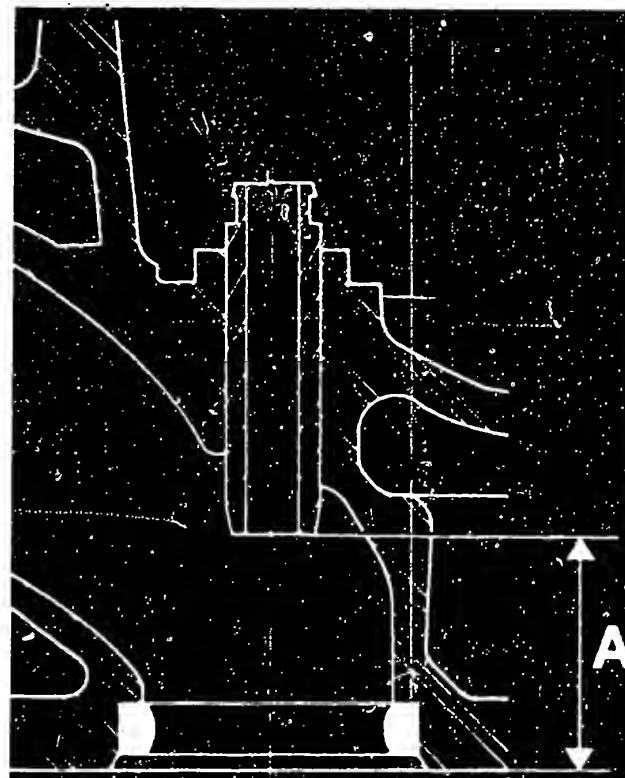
Dieselmotor J8S: Das Einbaumaß A für die Ventilführung beträgt 32,5mm.
